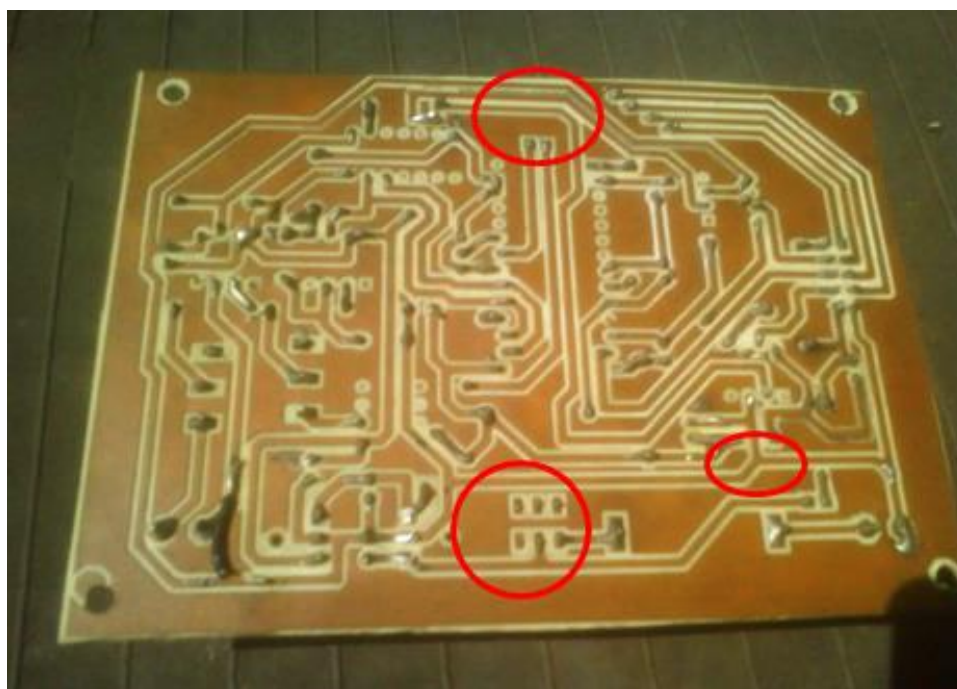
Irregularidades en una PCB hecha con Fresa CNC.
